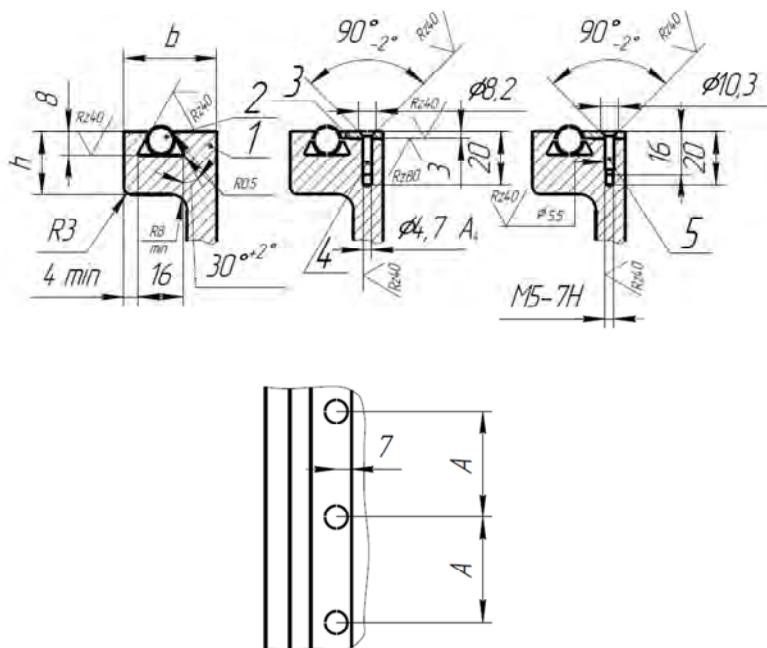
Конструкции паза под резиновый уплотнитель:
